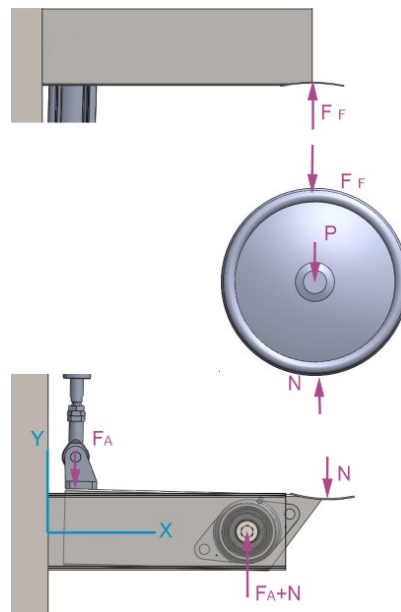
Fuerzas a través de conjunto móvil, barril y pieza fija.
